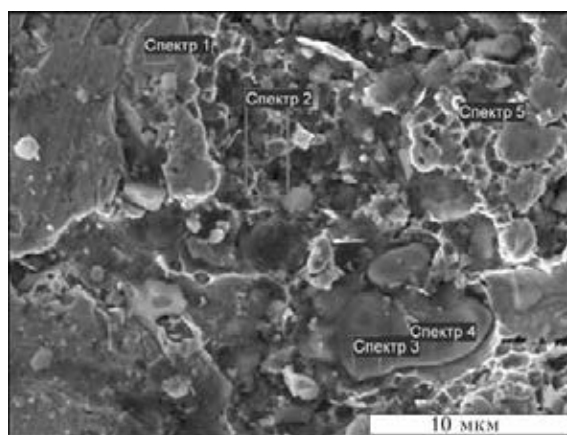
Непровар на поверхности излома сварного соединения рельсов
